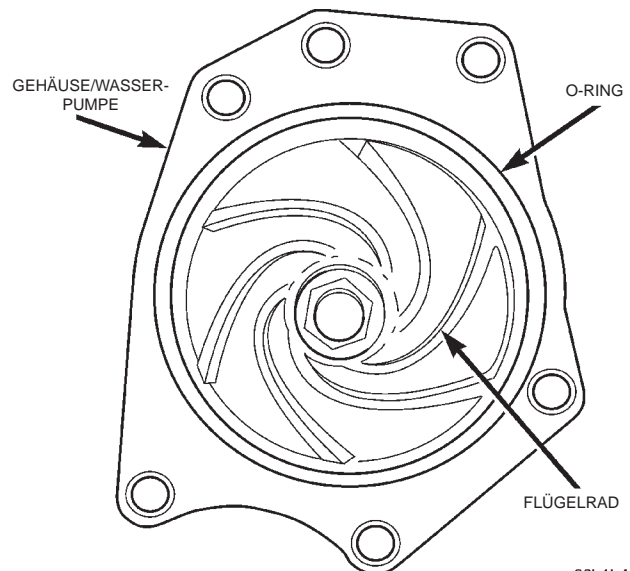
Gehäuse der Wasserpumpe—3.2L-Motor
